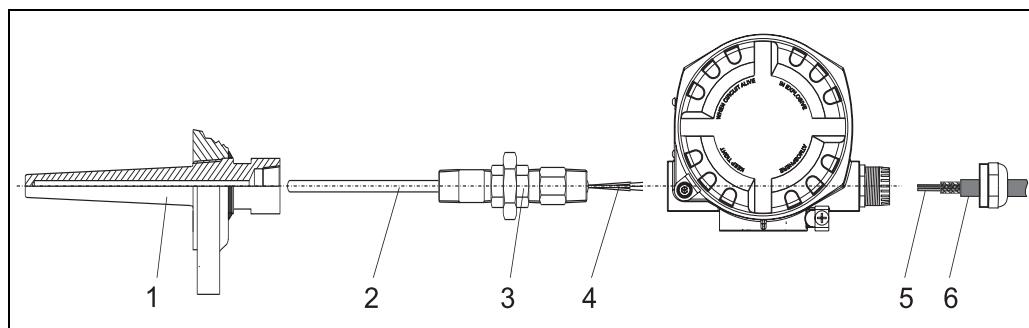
Direkte Montage des Feldtransmitters am Sensor
